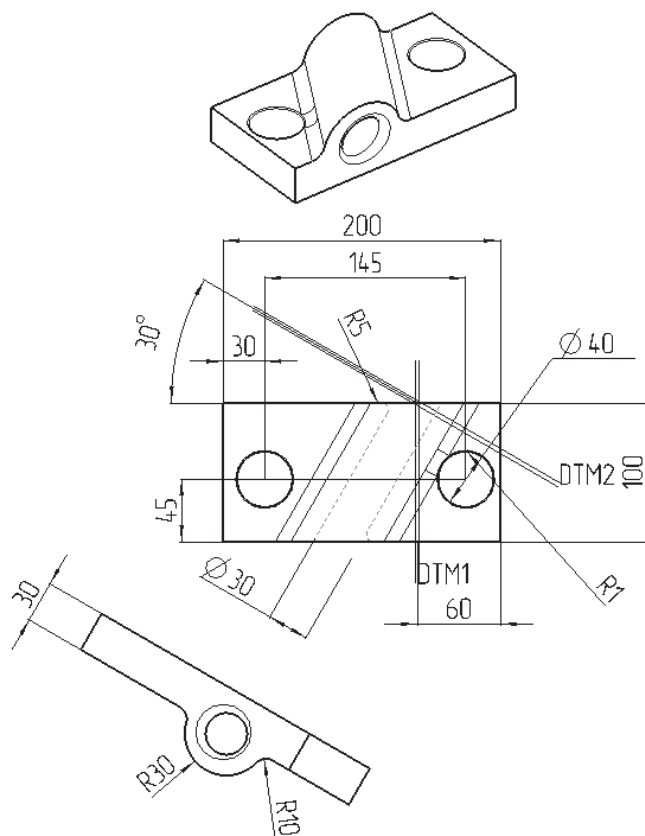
Общий вид и габаритные размеры кронштейна
